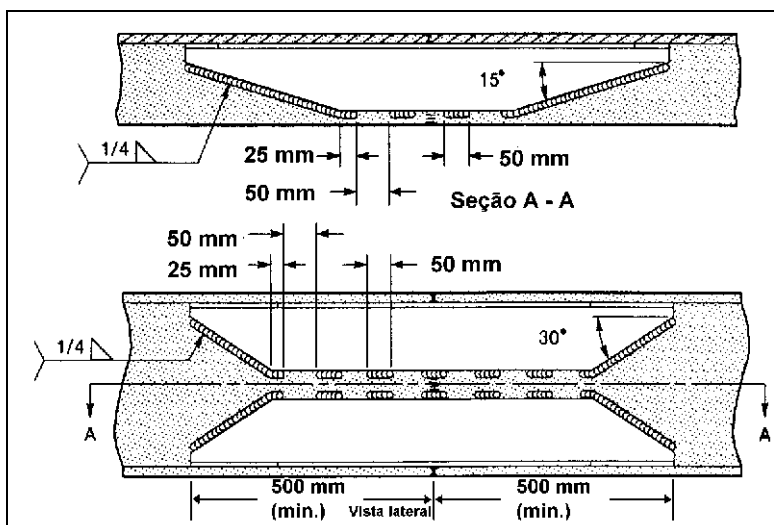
Fijación de los refuerzos mediante soldadura
